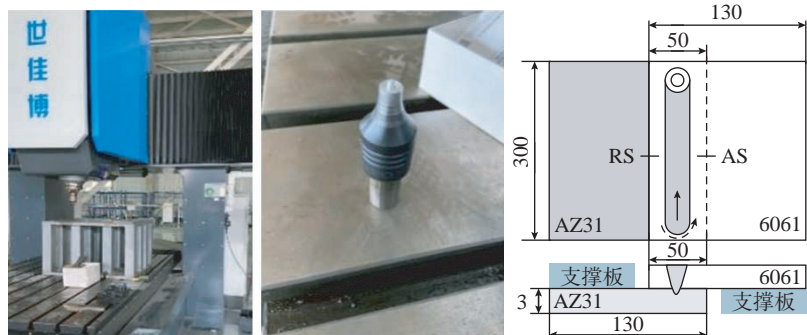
FSW 设备和搅拌头及焊接过程(mm)
